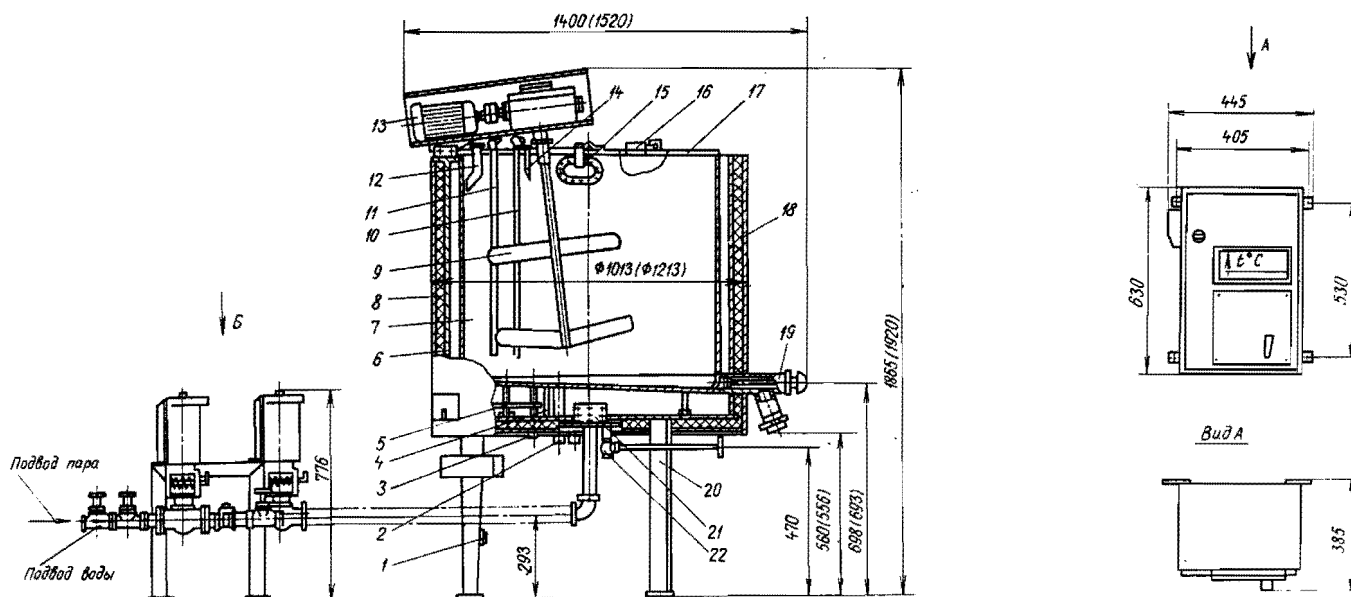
Общий вид установки заквасочной марки ОЗУ-300(ОЗУ-600):
